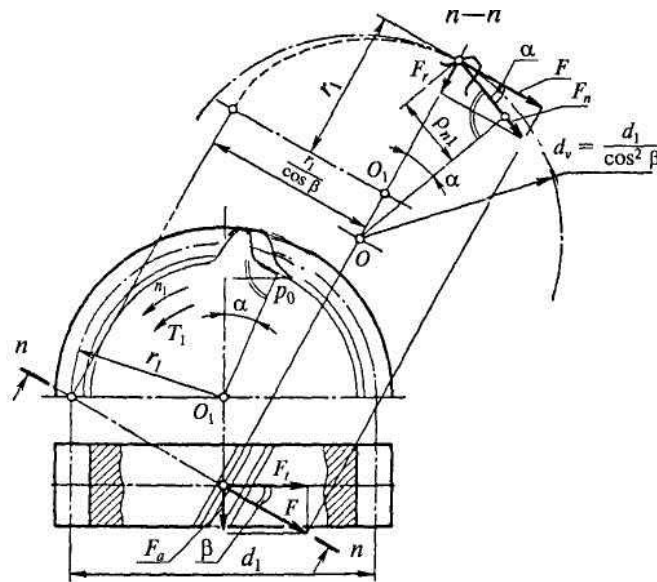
Параметры приведенного (эквивалентного) колеса
